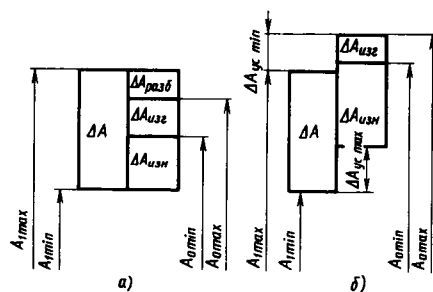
Схема допусков на исполнительные размеры режущих инструментов при разбивке (а) и усадке (б)
